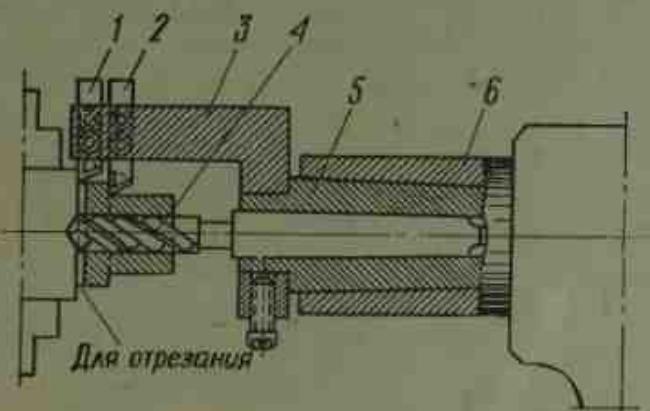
Совмещение переходов при обработке ступенчатой поверхности и сверлении детали:
